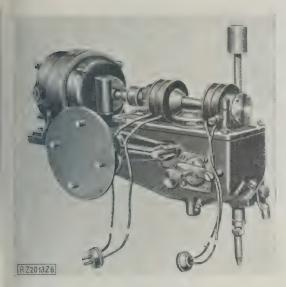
Schweißkopf der General Electric Co., geöffnet.
